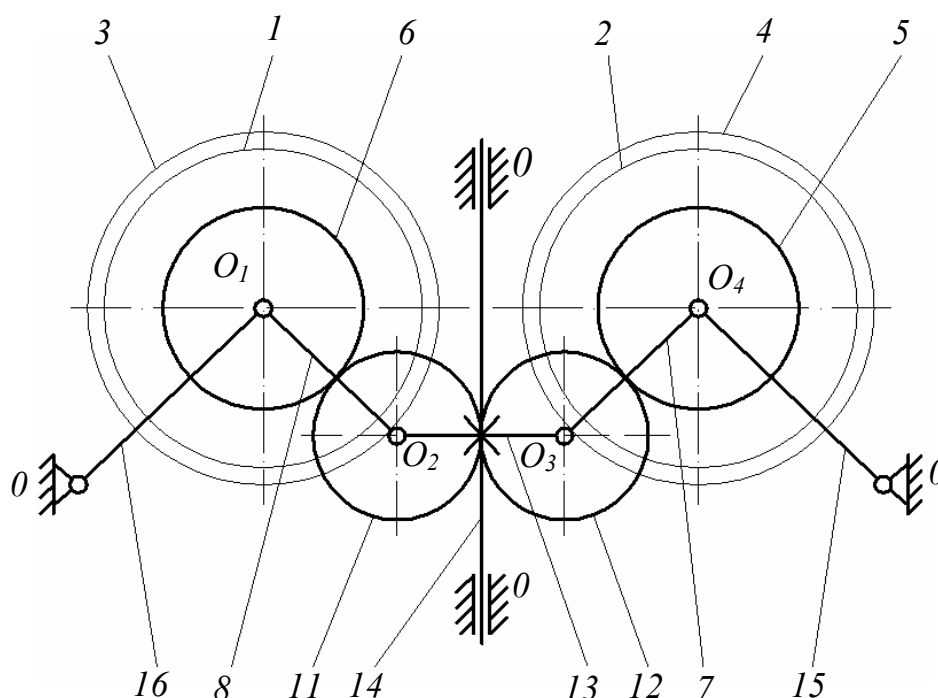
Второй вариант новой конструкции механизма привода валковой пары
